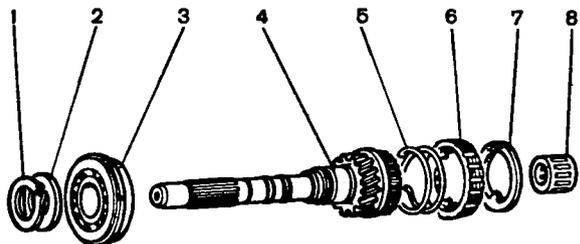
Детали первичного вала: 1 - стопорное кольцо; 2 - пружинная шайба; 3 - подшипник; 4 - первичный вал; 5 - пружина синхронизатора; 6 - блокирующее кольцо синхронизатора; 7 - стопорное кольцо; 8 - подшипник
